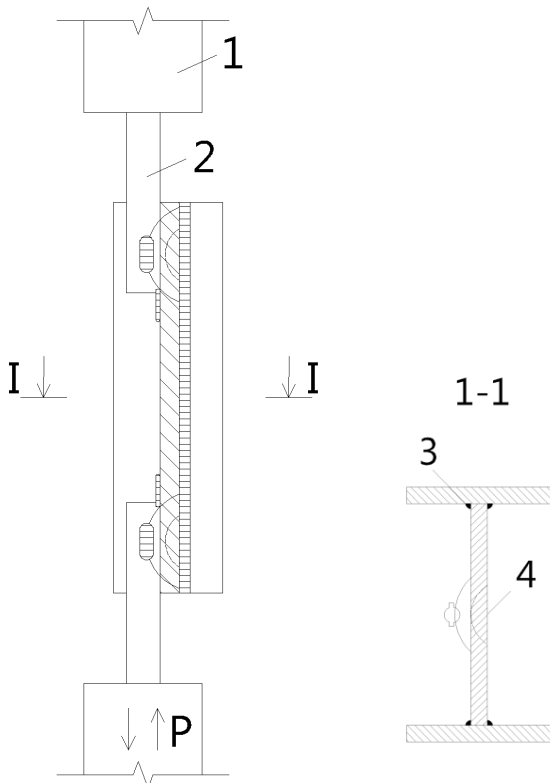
Опытный образец с двумя нахлесточными соединениями, выполненными контактной точечной сваркой по рельефу:
